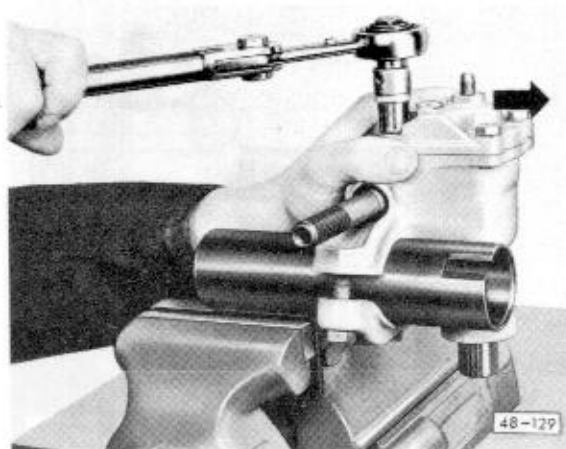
Einstellschraube mit Scheibe in Lenkrollenwelle einbauen
